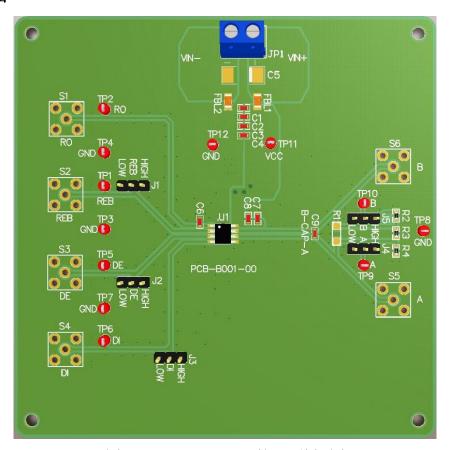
CA-IF48xxHS PCB 的 3D 俯视图
